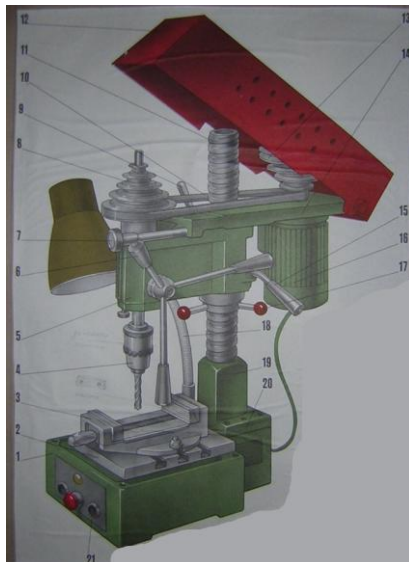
Настільний вертикально-свердильний верстат 2м112. Будова: 1 – основа; 2 – робочий стіл; 3 – лещата; 4 – патрон; 5 – корпус; 6 – рукоятка подачі; 7 – гвинт регулювання натягу паси; 8 – шків ведений; 9 – важіль затискання; 10 – пас клиновидний; 11 – колона; 12 – захисний кожух; 13 – шків ведучий; 14 – плита над двигуном; 15 – рукоятка фіксації корпусу; 16 – електродвигун; 17 – рукоятка вертикального переміщення корпусу; 18 – кронштейн лампи світильника
